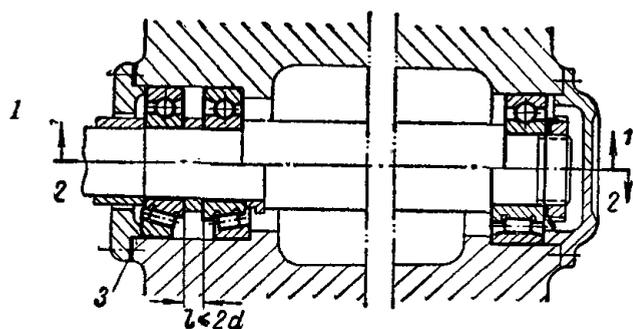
Схема установки радиально-упорных подшипников по два в одной опоре
